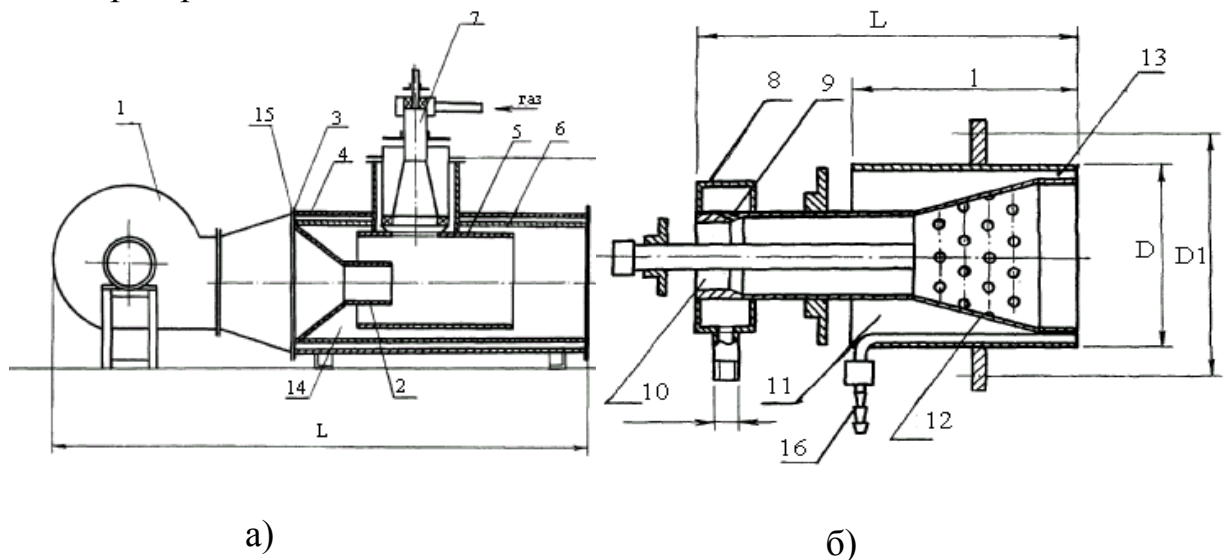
Теплогенератор рециркуляційний газовий: а) принципова схема установки; б) конструктивна схема пальника багатостадійного спалювання.
